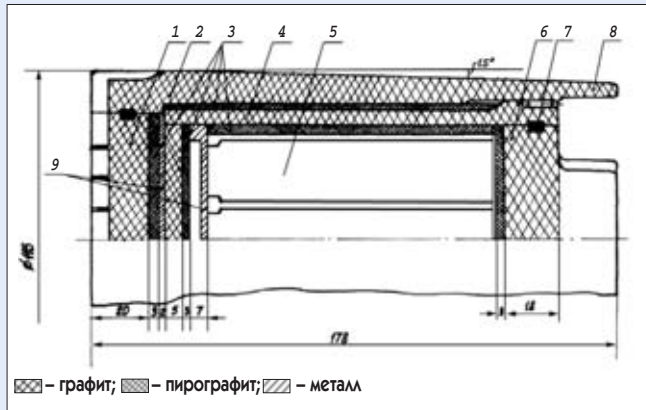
Конструктивная схема кассеты: 1 – передняя пробка; 2 – наружный корпус; 3 – прокладки; 4 – внутренний корпус; 5 – ампульная зона; 6 – задняя пробка; 7 – замок; 8 – стабилизаторы; 9 – балансировочный груз
